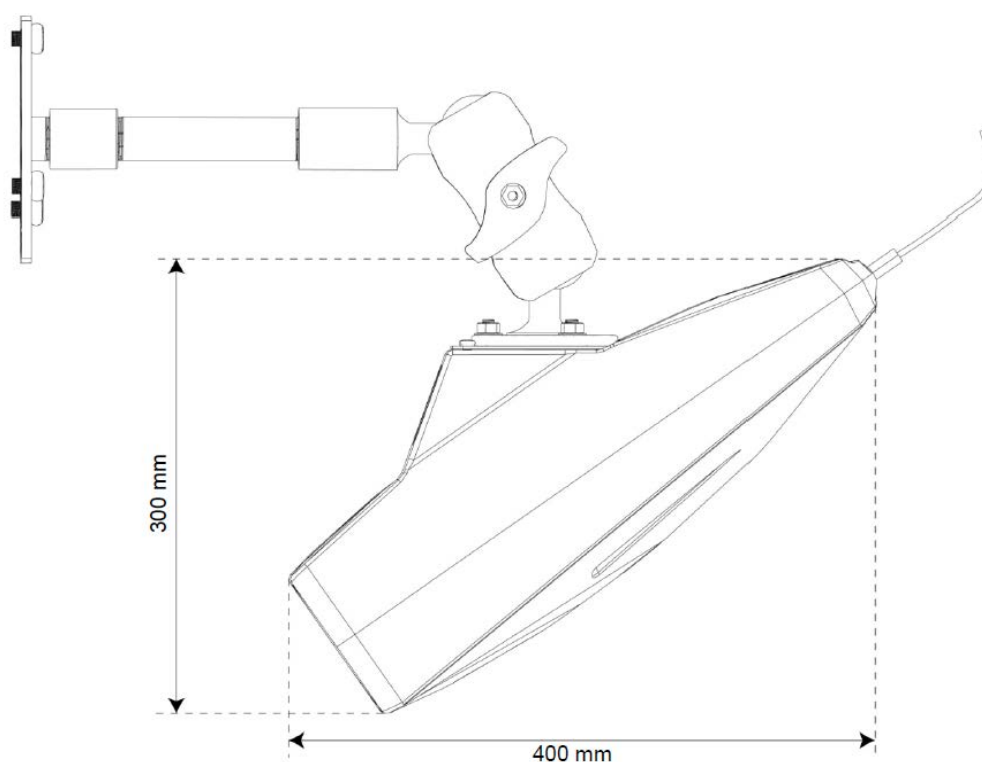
Vista lateral de las dimensiones del sensor RAVEN EYE según se ha instalado
